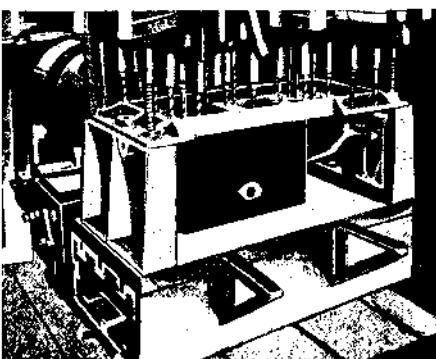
Сверление блока цилиндра на приспособлении пригодном для сверления поддона.
